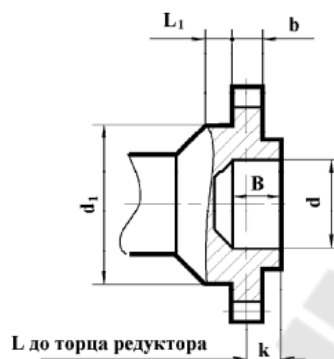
Размеры концов выходных валов в виде зубчатой полумуфты
